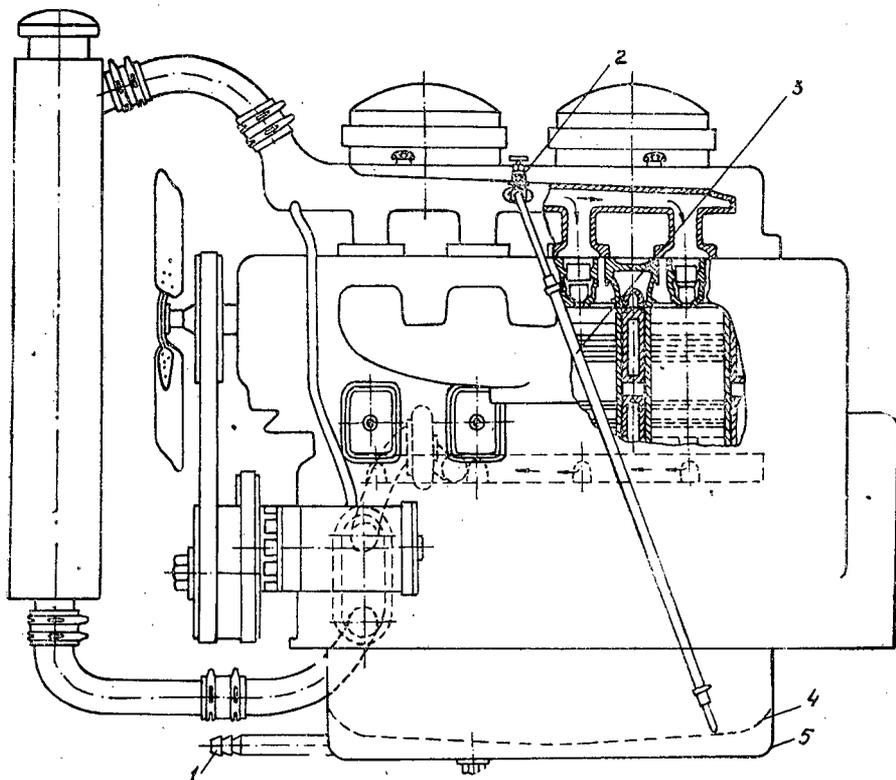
Схема размещения оборудования для предпускового обогрева паром дизельных двигателей ЯАЗ-204:
